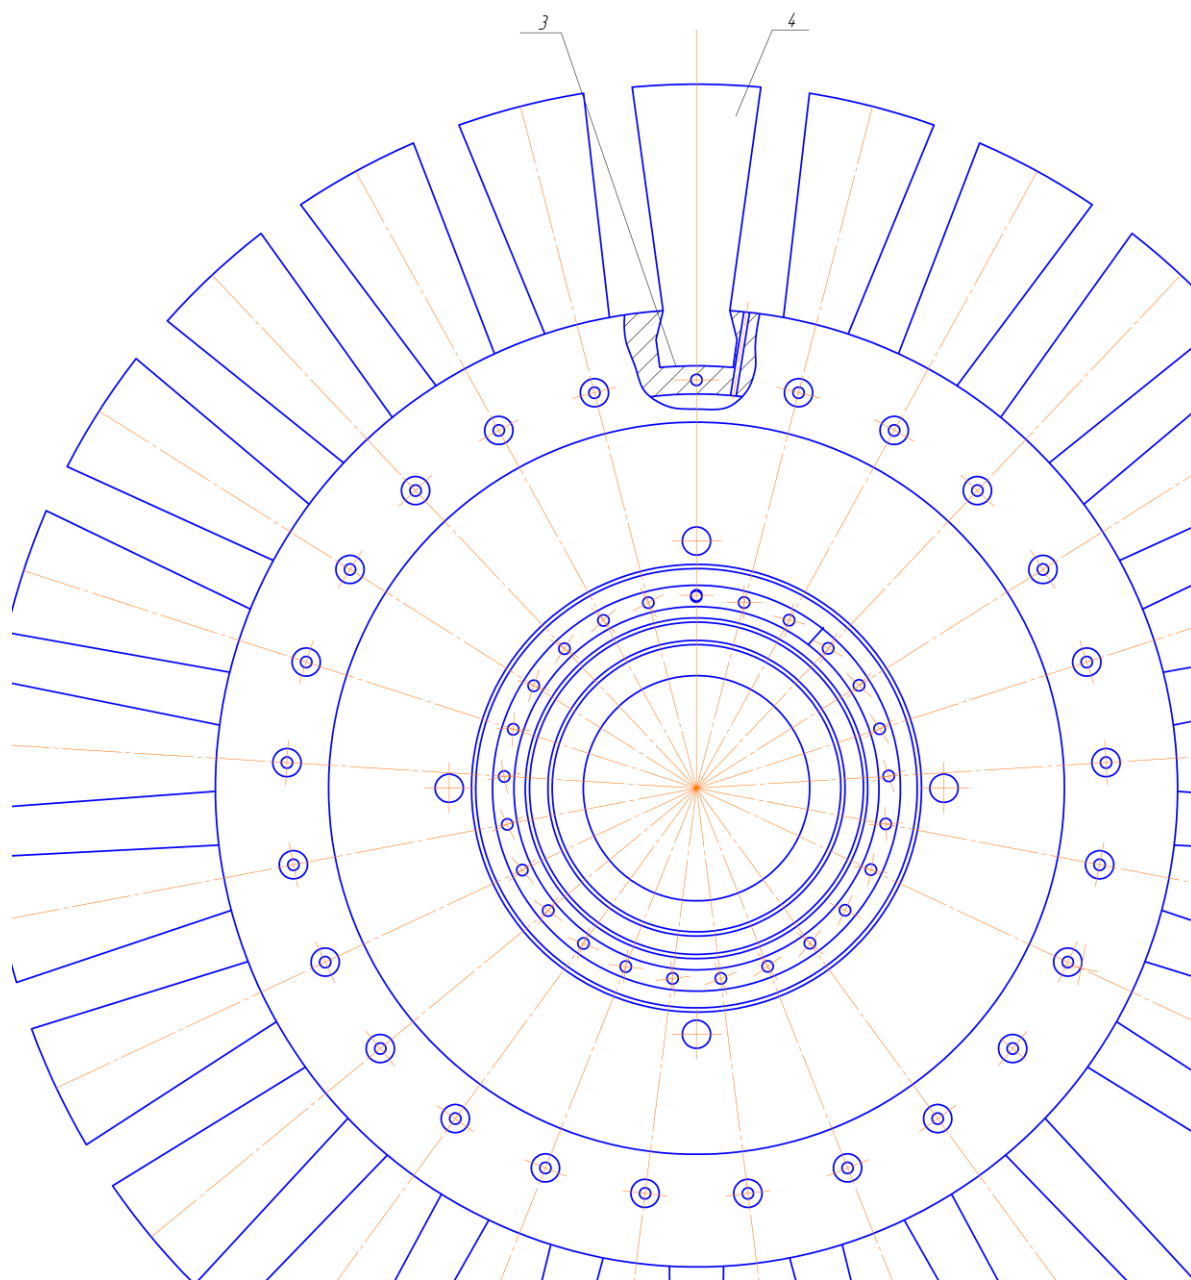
Вид спереди на дискретный абразивный инструмент
